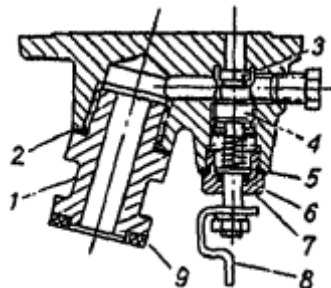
Наполнительный вентиль для легковых автомобилей ГАЗ-24-17
